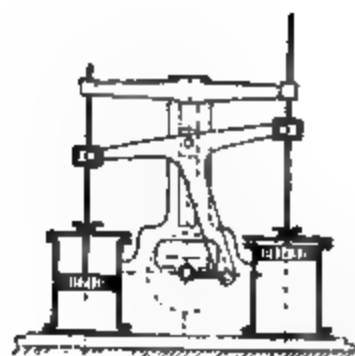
Zwillings- oder Compoundmaschine, Pat. Bernay. Vorteile würden sein: Geringes Gewicht und geringe Höhe. Nachteile unter anderen: Schleifen an den Kolbenstangen.
